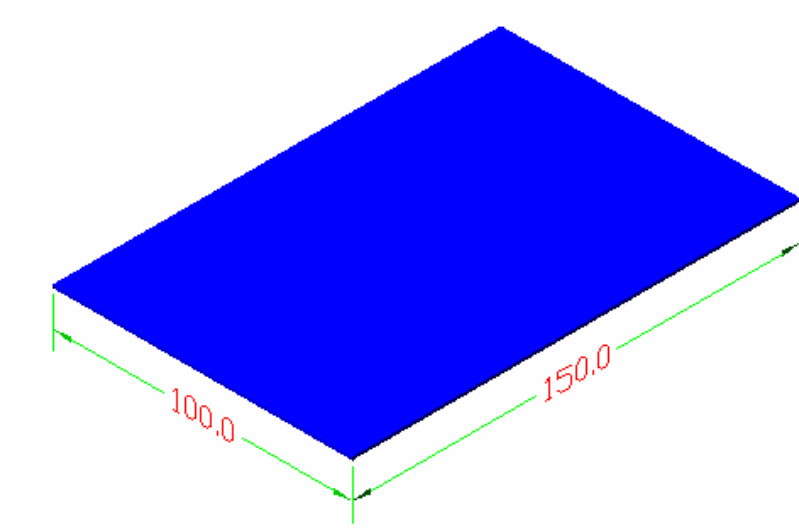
Geometría de las Probetas de lámina de acero descubierto y lámina de zinc. Medidas en mm.
